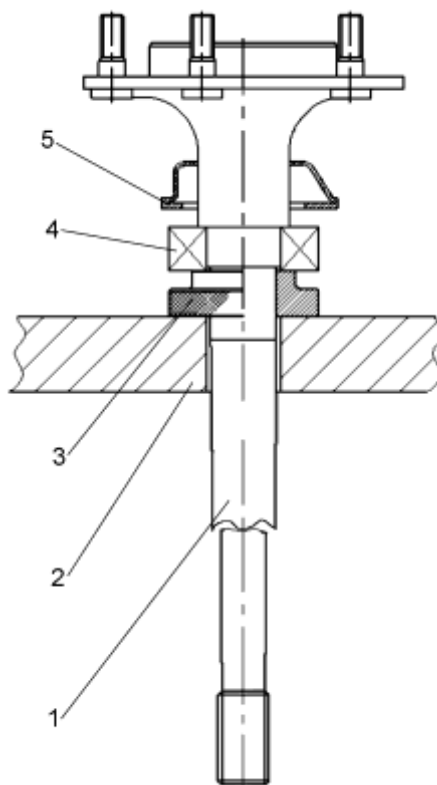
Выпрессовка запорного кольца подшипника полуоси:
